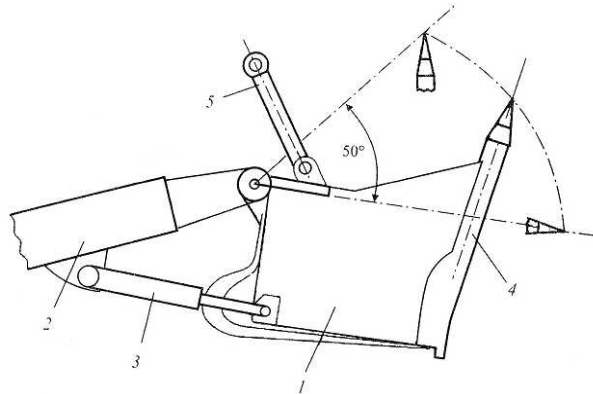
Схема поворотного ковша активного действия (КАД): 1 – ковш; 2 – рукоять экскаватора; 3 – гидроцилиндр поворота ковша; 4 – пневмоударник; 5 – элемент подвески ковша [13]
